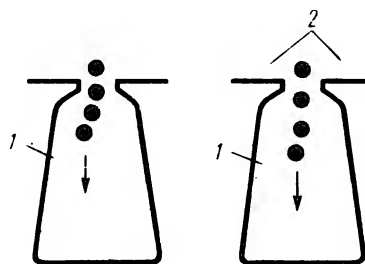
Пазовый короб и вкладыши для укладки обмотки:
